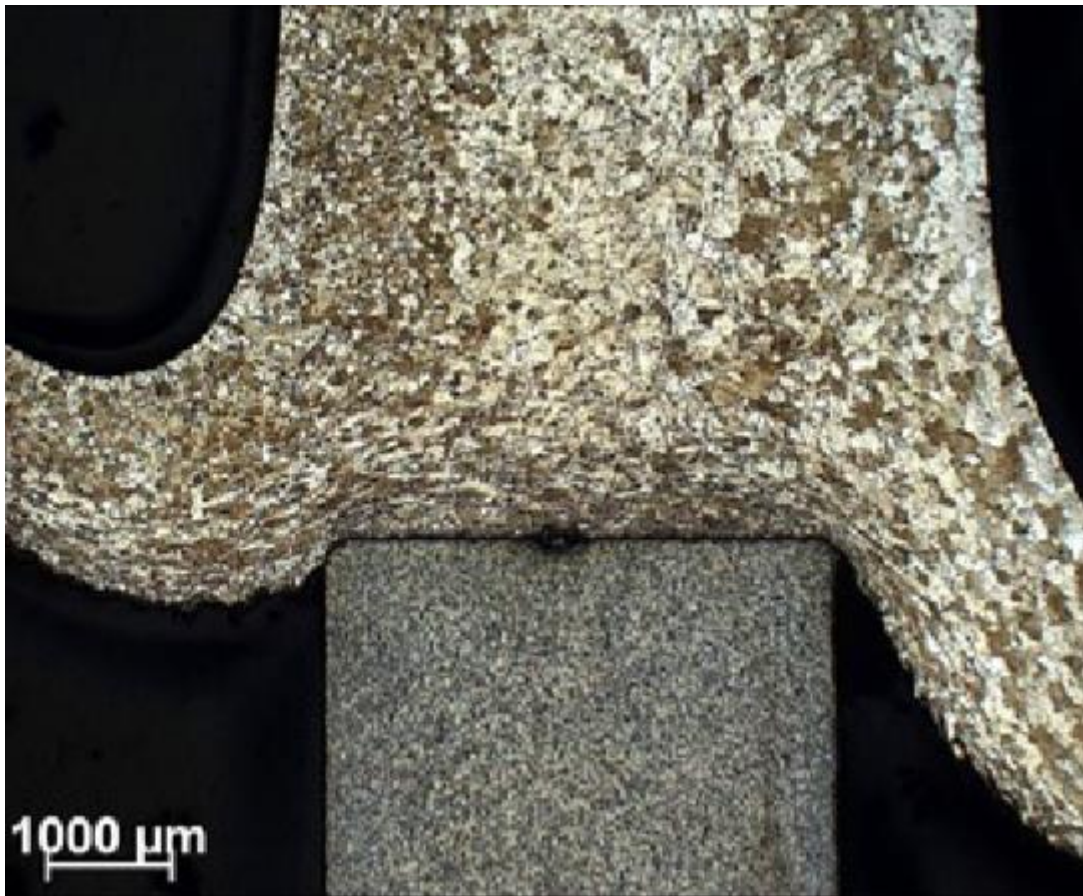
Arbres de transmission soudés par friction
